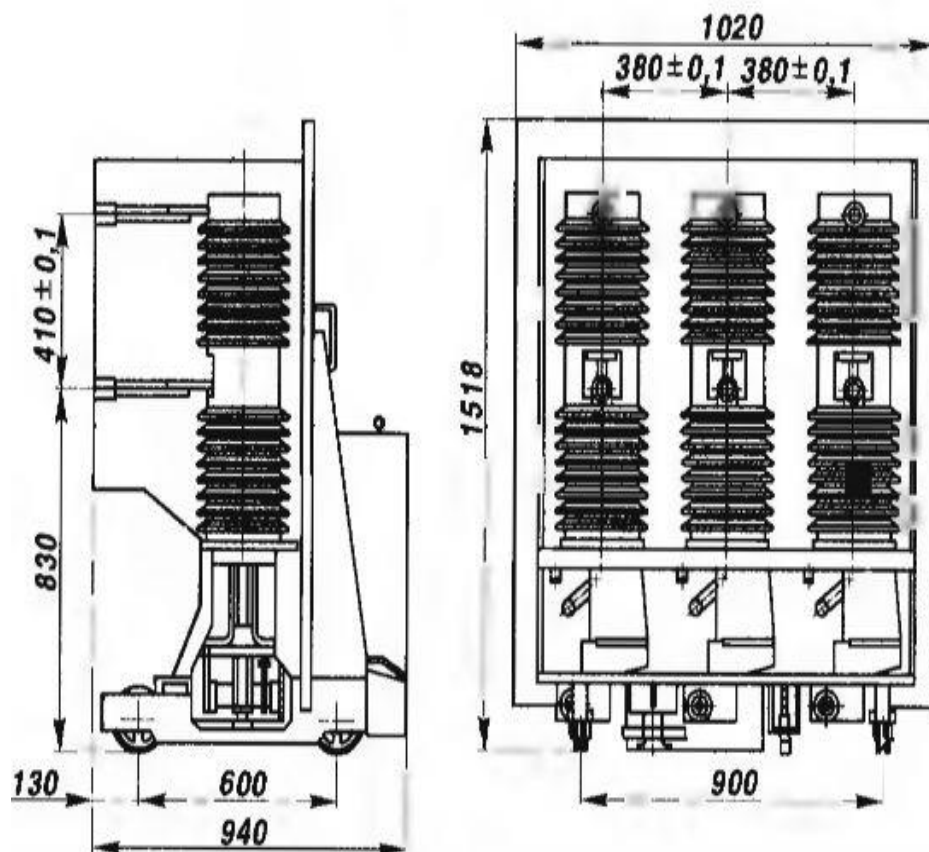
Размеры выключателя типа ВБЭК-10-31,5/2500
